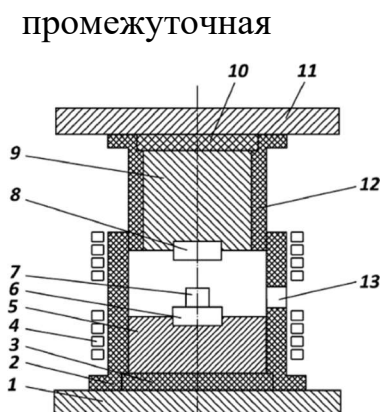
Принципиальная схема штампа для изотермической штамповки с кожухом [39]: 1 - нижняя опорная плита; 2 - нижний подвижный кожух; 3 – нижняя прокладка; 4 - индуктор; 5 - нижний штамподержатель; 6 - нижний штамп; 7 - заготовка; 8 - верхний штамп; 9 - верхний штамподержатель; 10 - верхняя прокладка; 11 - верхняя опорная плита; 12 - кожух; 13 – окно
